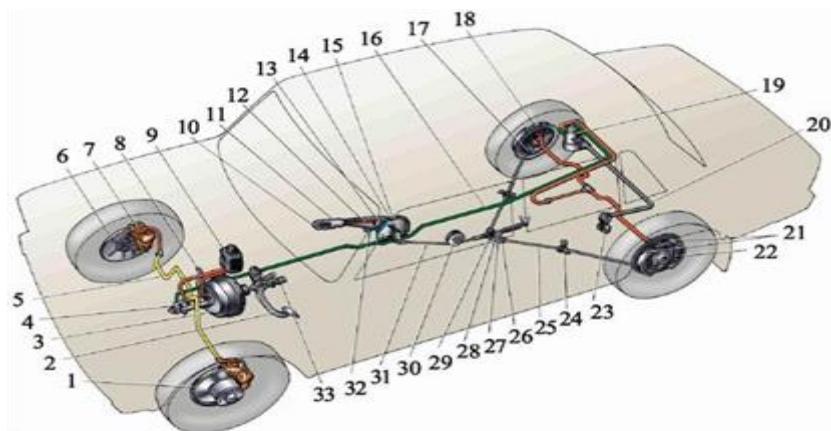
Общая схема тормозной системы: 1 – передний тормоз; 2 – педаль тормоза; 3 – вакуумный усилитель; 4 – главный цилиндр гидропривода тормозов; 5 – трубопровод контура привода передних тормозов; 6 – защитный кожух переднего тормоза; 7 – суппорт переднего тормоза; 8 – вакуумный трубопровод; 9 – бачок главного цилиндра; 10 – кнопка рычага привода стояночного тормоза; 11 – рычаг привода стояночного тормоза; 12 – тяга фиксатора рычага; 13 – фиксатор рычага; 14 – кронштейн рычага привода стояночного тормоза; 15 – возвратный рычаг; 16 – трубопровод контура привода задних тормозов; 17 – фланец наконечника оболочки троса; 18 – задний тормоз; 19 – регулятор давления задних тормозов; 20 – рычаг привода регулятора давления; 21 – колодки заднего тормоза; 22 – рычаг ручного привода колодок; 23 – тяга рычага привода регулятора давления; 24 – кронштейн крепления наконечника оболочки троса; 25 – задний трос; 26 – контргайка; 27 – регулировочная гайка; 28 – втулка; 29 – направляющая заднего троса; 30 – направляющий
